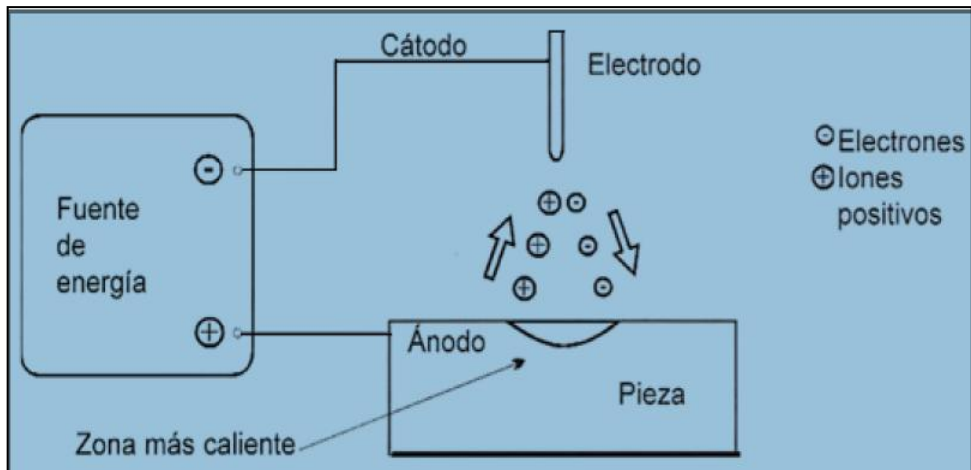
Uso de la polaridad inversa en la soldadura de aluminio.
